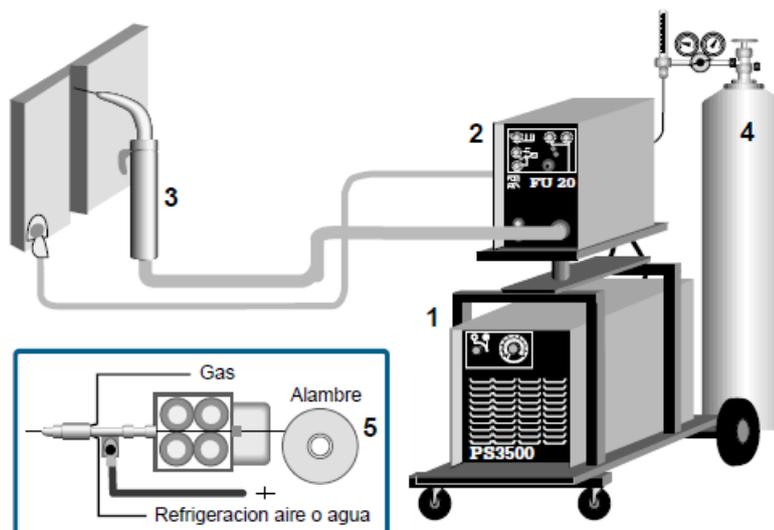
Esquema de equipo de soldadura tipo MAG. [10]
